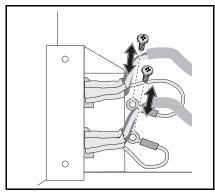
Extracción e instalación de los cables del plano posterior
